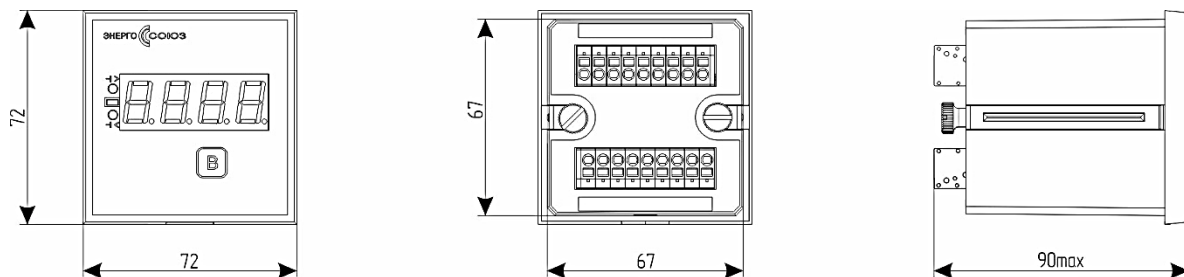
Габаритные и установочные размеры конструктивного исполнения М
